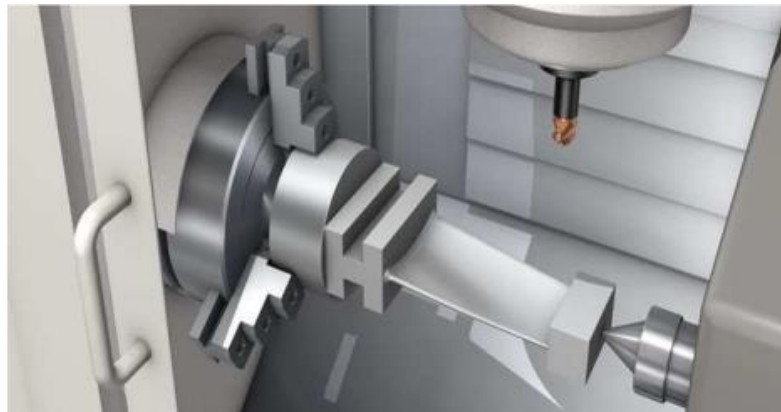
Usinage d'une aube de turbine sur la machine cinq axes
